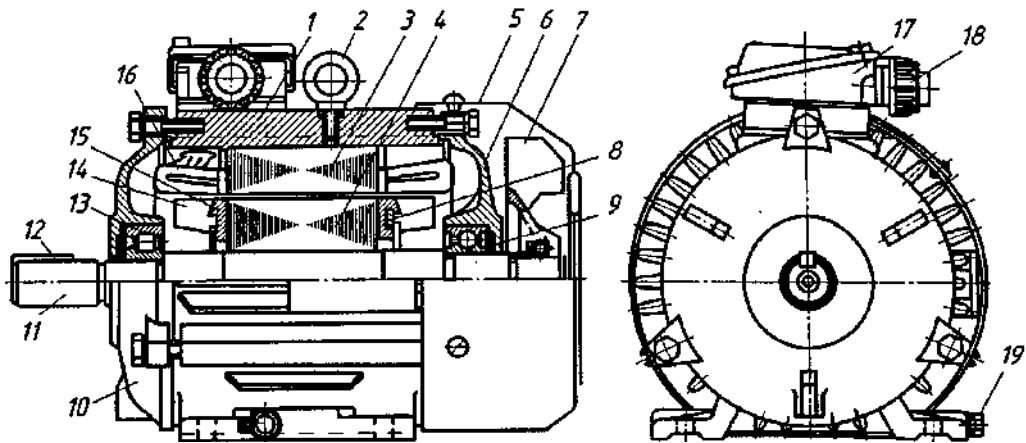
Асинхронный двигатель с короткозамкнутым ротором:
